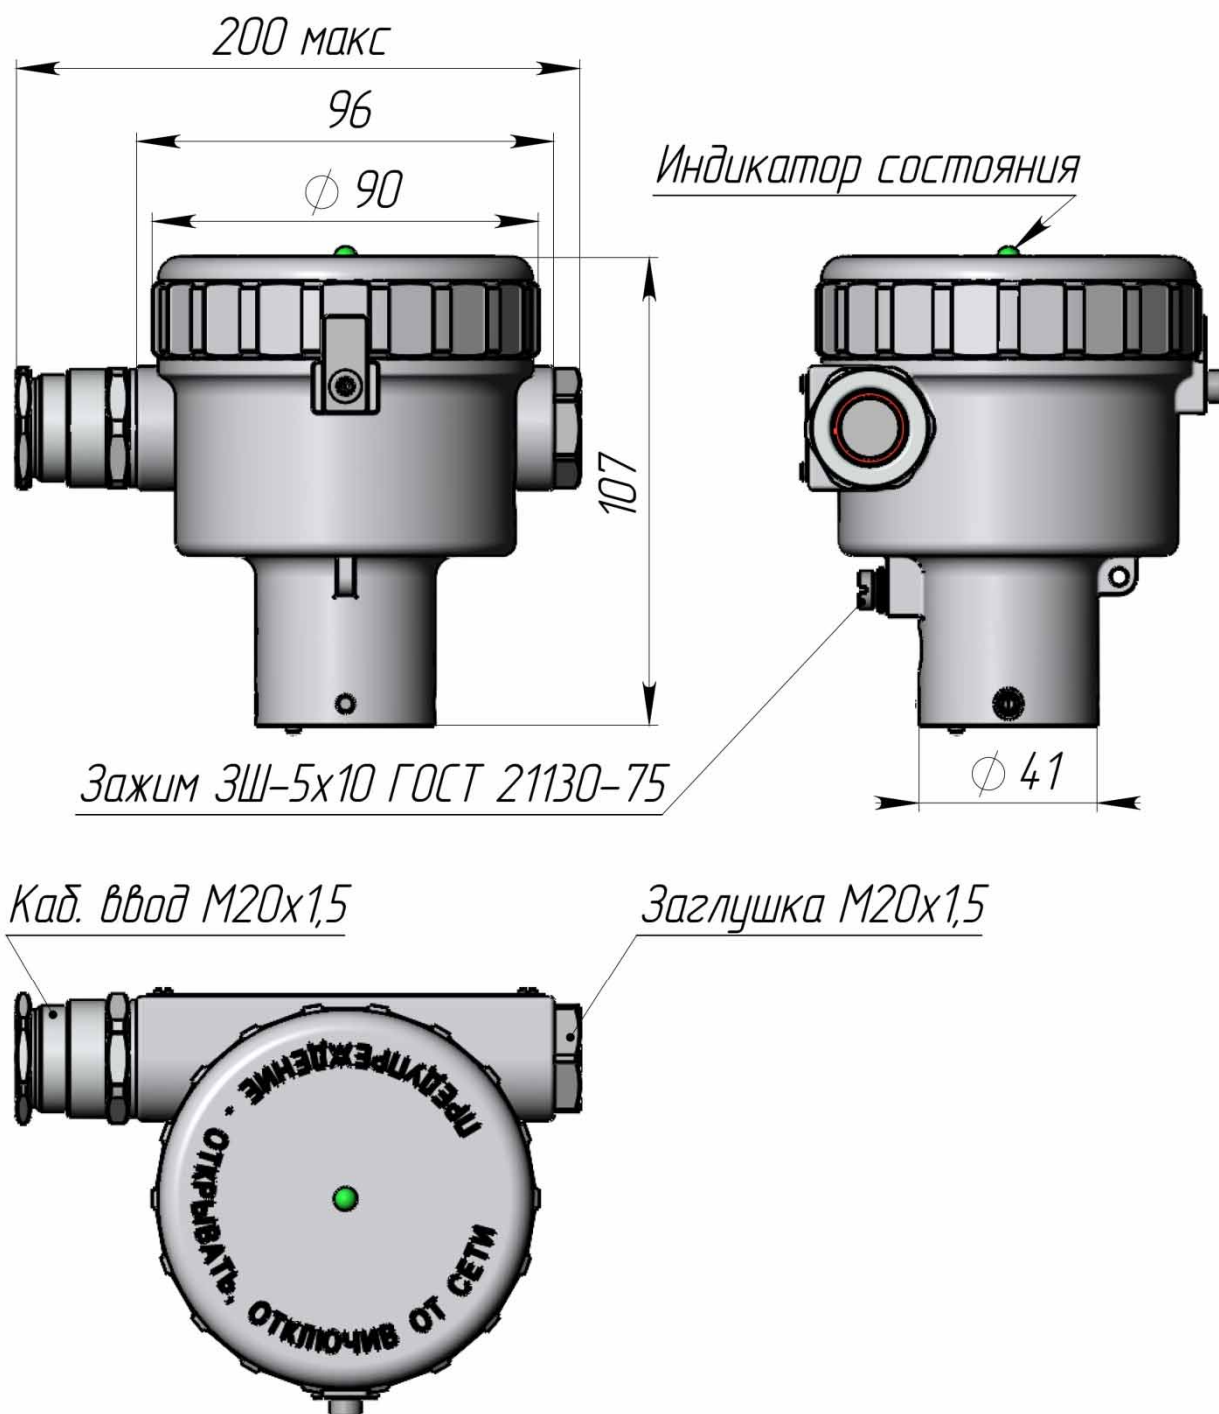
Габаритные размеры корпуса блока электронного в корпусе из алюминиевого сплава с полиуретановым покрытием для общепромышленного применения
